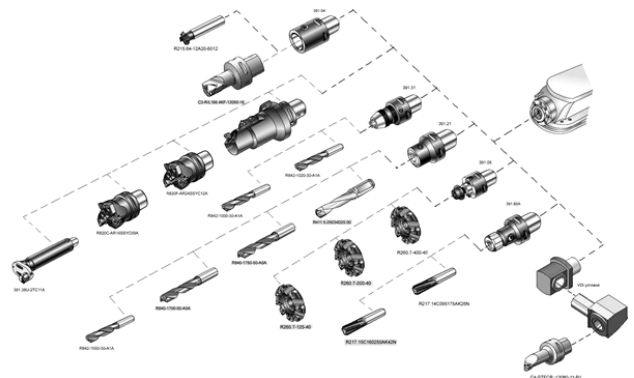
Виды инструментальной оснастки для обработки детали «Корпус редуктора»
